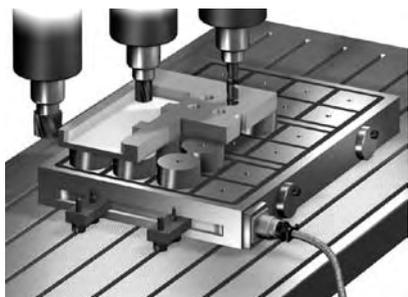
А - чистовая обработка плоских поверхностей, сверление, выполнение отпечатков
